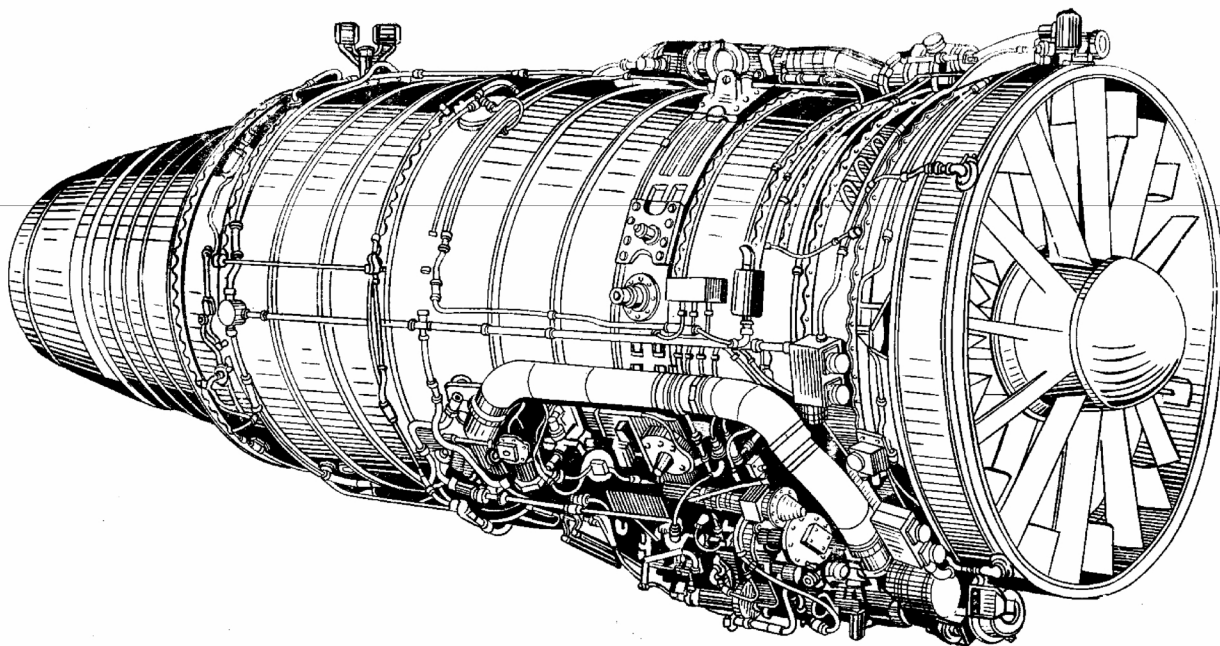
Двигатель НК-8-2У с соплом (вид справа)
